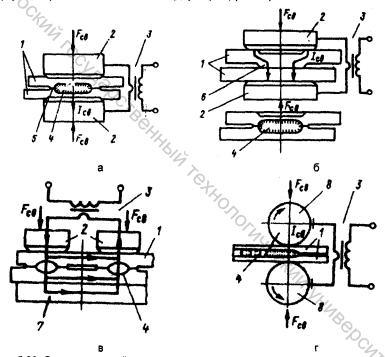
Схемы точечной сварки: а – двусторонняя; 6 – рельефная; в – односторонняя; г – шовная; 1 – свариваемые детали; 2 – электроды; 3 – трансформатор; 4 – жидкое ядро; 5 – уплотняющий поясок; 6 – выступ; 7 – медная подкладка; 8 - ролики
